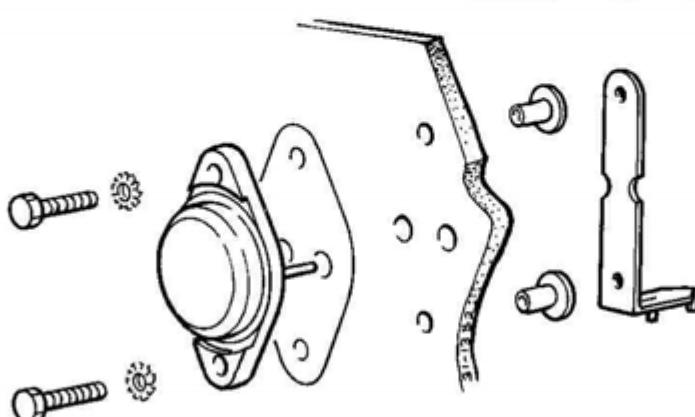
Montering av slutt-transistor, husk silikonfett på begge sider av glimmerskiven.
